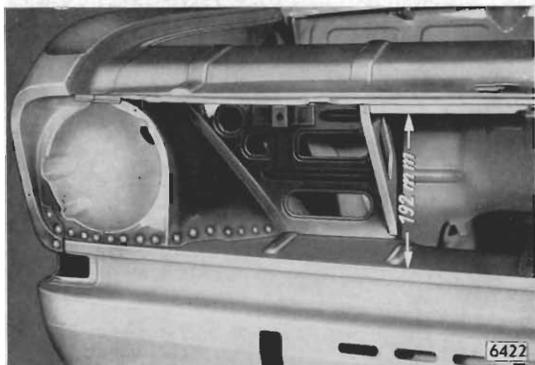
Unteres Luftleitblech an Lampengehäuse punktgeschweißt und an Kotflügel autogeschweißt
